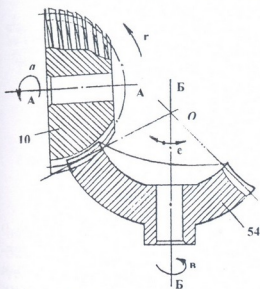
Схема нарезания конического колеса с наружными зубьями
